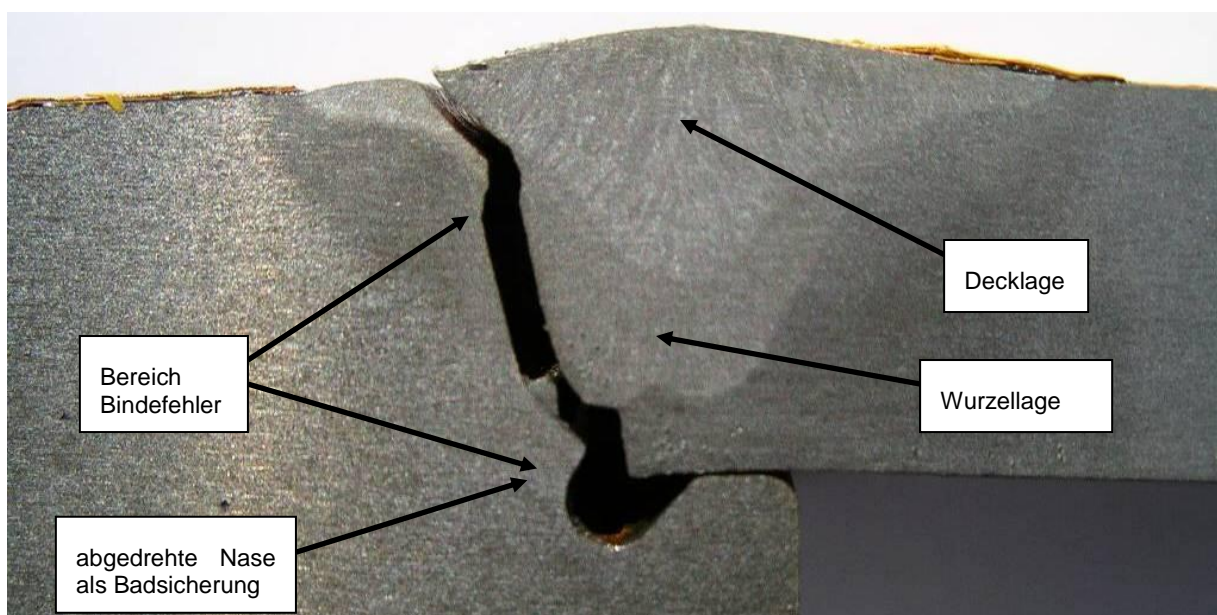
Schlibbild durch die Schweißverbindung (max. 20% der Flanke aufgeschmolzen)
